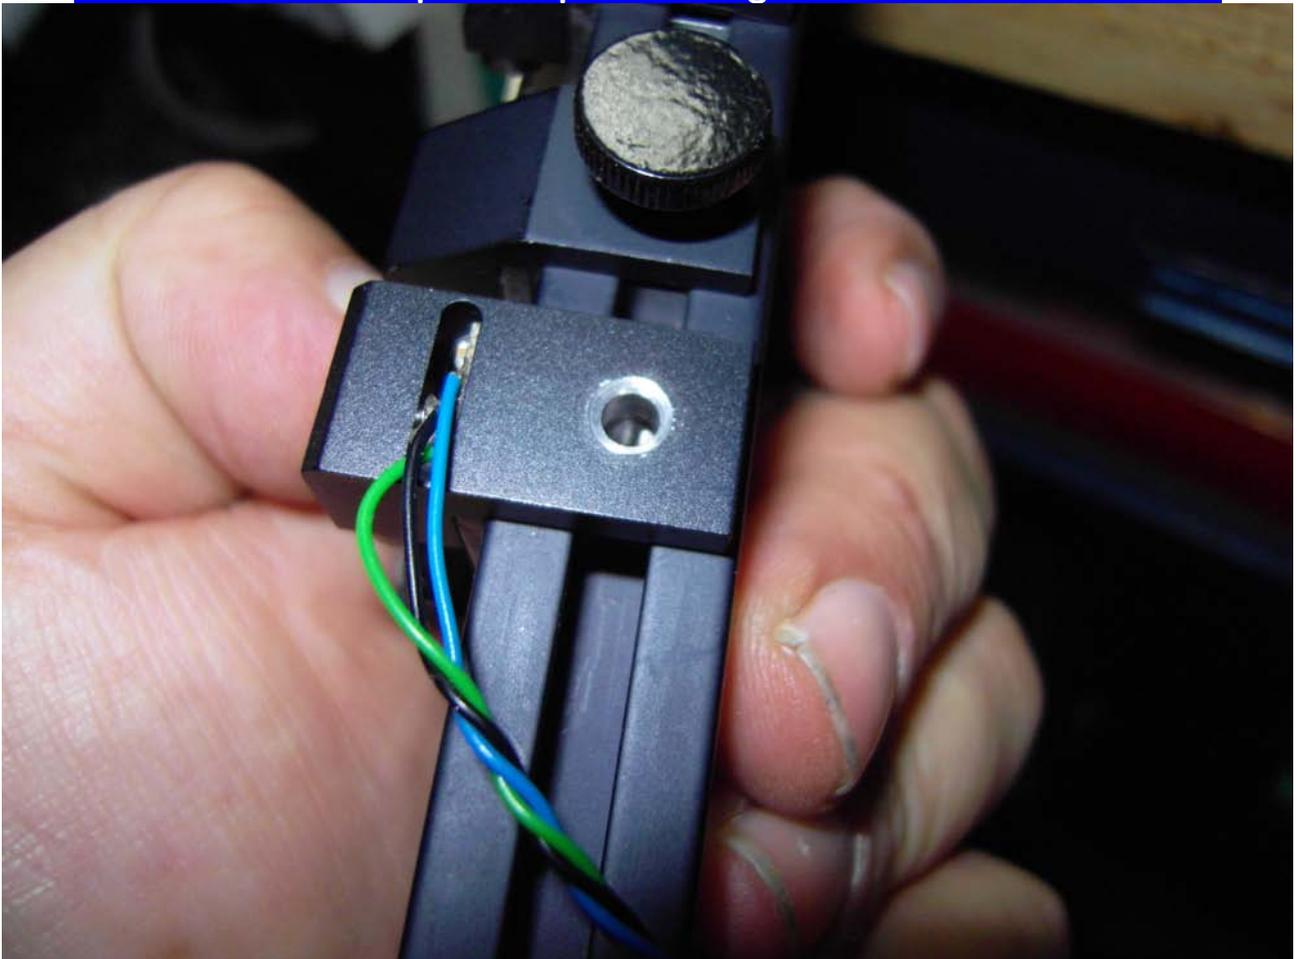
i 3 cavetti per il collegamento al contakilometri
